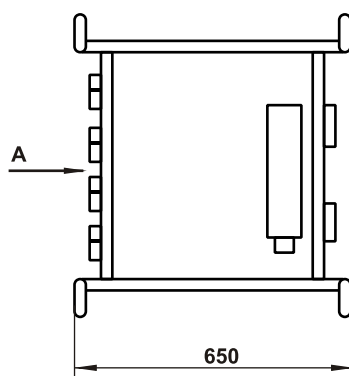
Вид в разрезе шкафа ШПТ (вид А для Рис. 1)
